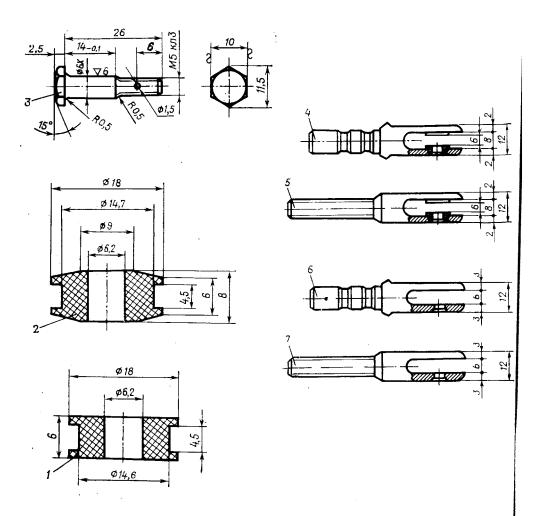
Детали соединений управления двигателем: 1 — резиновый вкладыш М65-261; 2 — резиновый вкладыш М65-262; 3 — болт М65-263 (М65.00.226); 4 — вилка Ш6500-215; 5 — вилка Ш6500-216; 6 — вилка Ш6500-217; 7 — вилка Ш6500-218
